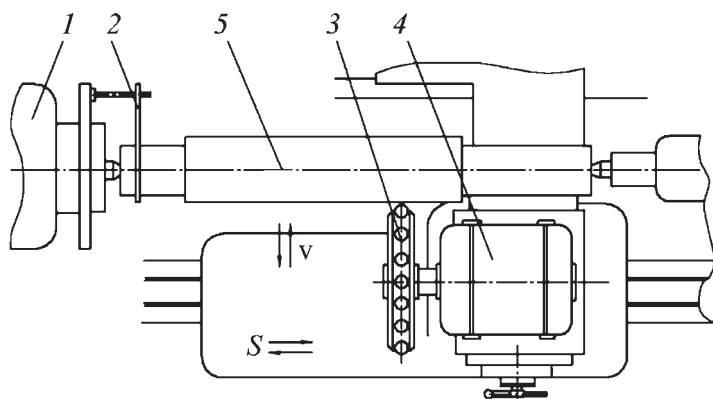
Схема ЦО наружной цилиндрической поверхности
